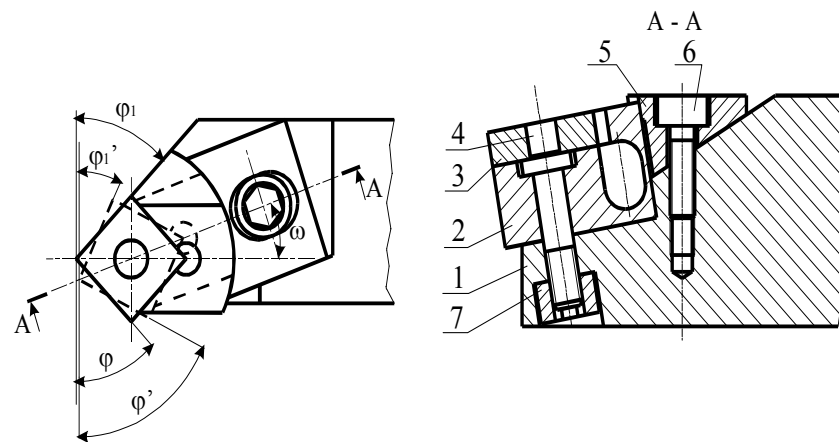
Универсально-сборный резец с изменяемой геометрией в плане
